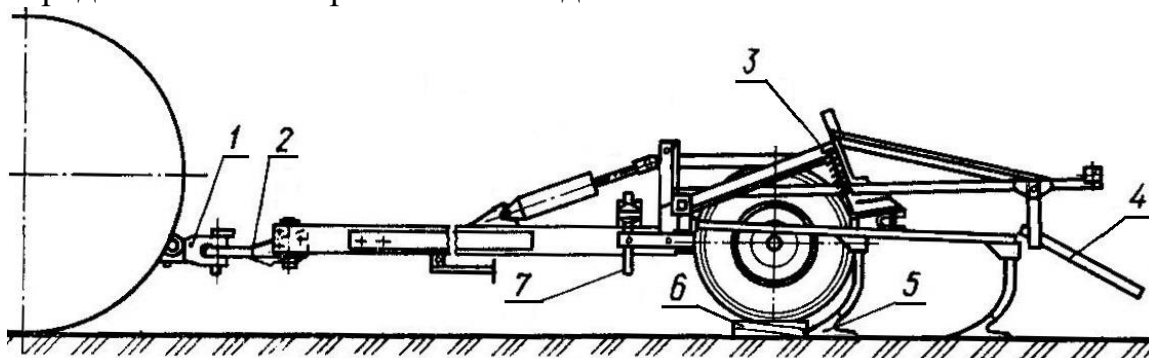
Схема встановлення культиватора на задану глибину обробітку:
